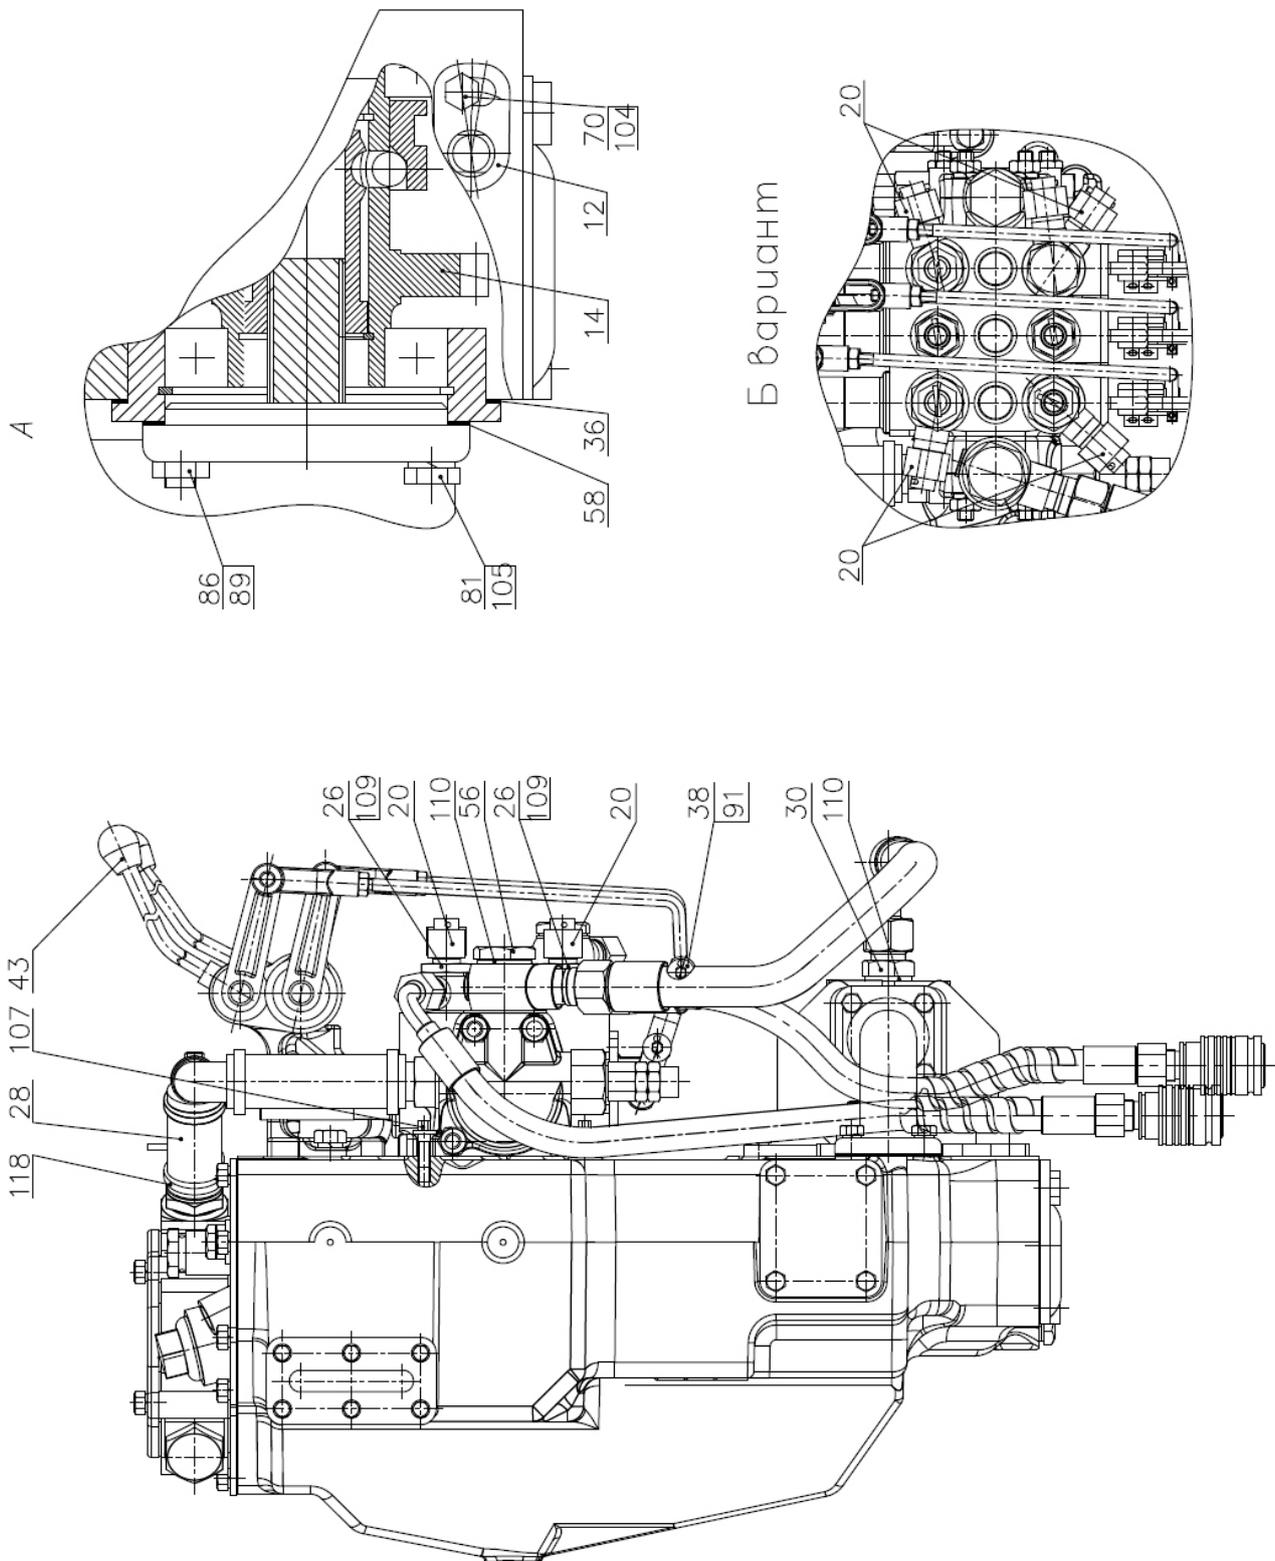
Корпус гидросистемы 900P-4600015-01 без силового регулятора (лист 2 из 2)
